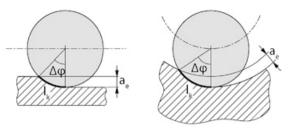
Kontaktlängen beim Rund- und Planschleifen / Lungimile de contact la rectificarea cilindrică și plană [SCH 18]
